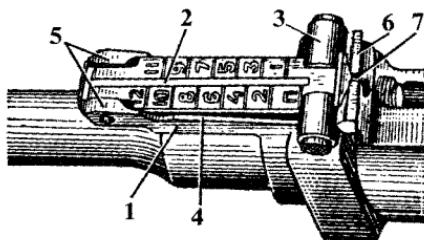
Механический (открытый) прицел СВД-63: 1 — колодка прицела; 2 — прицельная планка; 3 — хомутик; 4 — сектор; 5 — проушины; 6 — гравка прицельной планки; 7 — прорезь.
